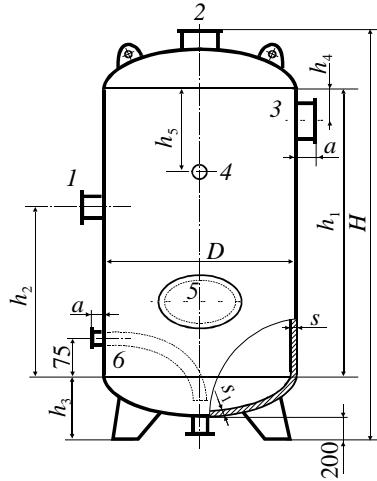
Воздухосборник (ресивер): 1 – выпускной патрубок; 2 – патрубок предохранительного клапана; 3 – выпускной патрубок; 4 – патрубок манометра; 5 – люк; 6 – патрубок-venting для продувки сосуда
